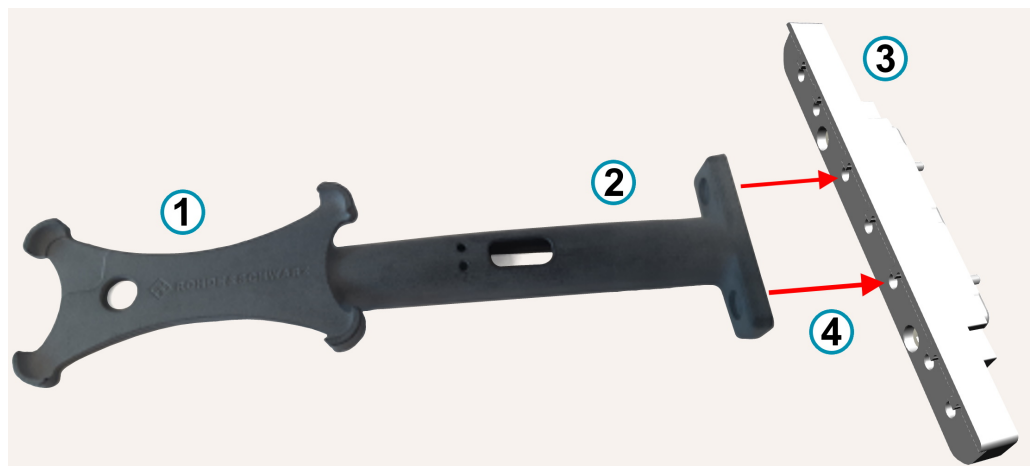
R&S CMQ-B719A "Drawer Fixture 2" Option, Bestellnummer 1537.6355.02
